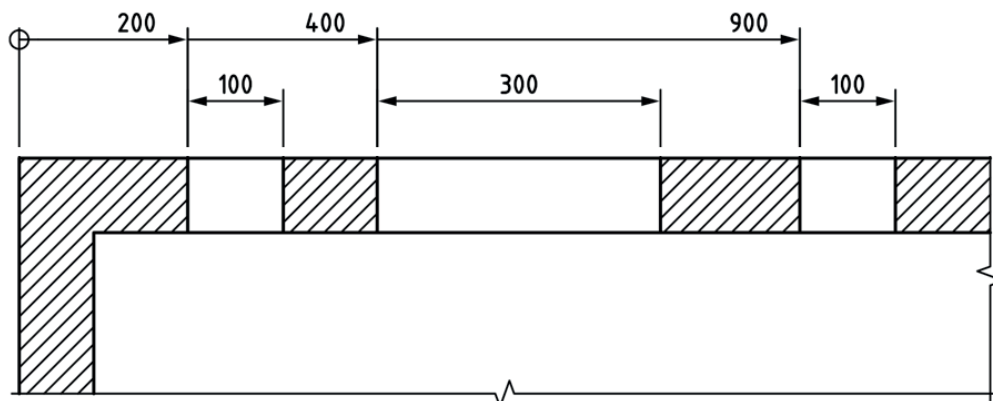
Cotagem combinada (aditiva e dimensões simples)
